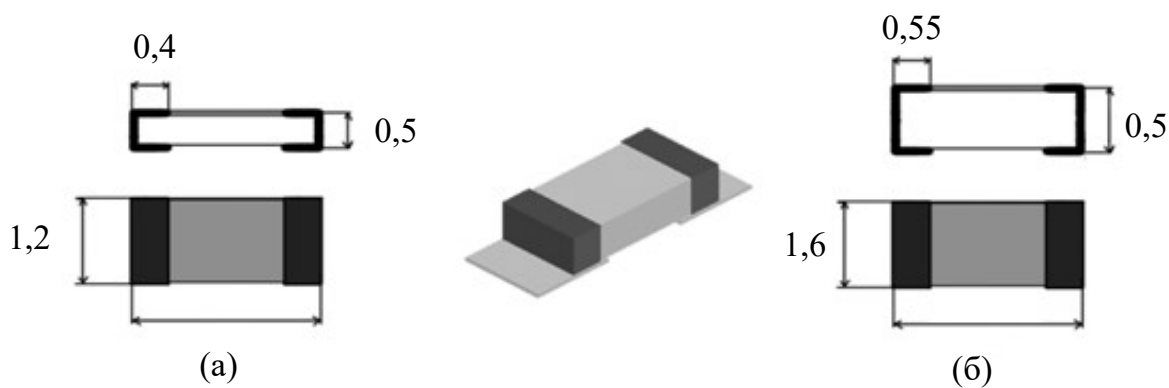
Габариты чип компонентов (мм) – типоразмера 0805 под (а) и типоразмера 1206 под (б)
